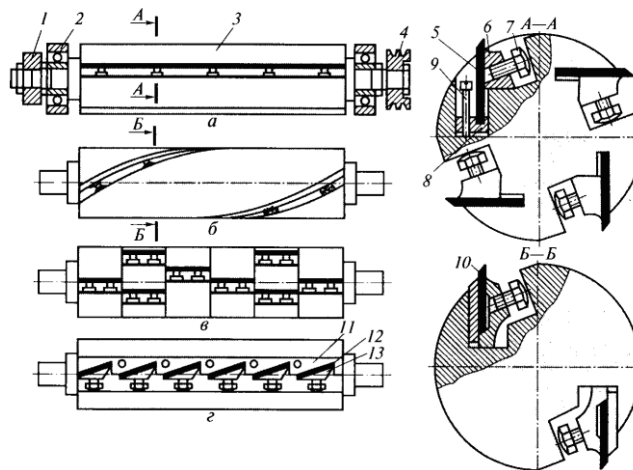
Ножові вали з різним розташуванням ножів: а – прямолінійним; б – гвинтовим; в – східчастим; г – східчастим з кутом нахилу ріжучої крайки; 1 – гальмовий шків; 2 – підшипник; 3 – корпус; 4 – приводний шків; 5, 12 – ножі; 6, 13 – притискні клини; 7 – гвинт; 8 – планка; 9 – регулювальний гвинт; 10 – плоский ніж з серповидною ріжучою крайкою; 11 – вставка
